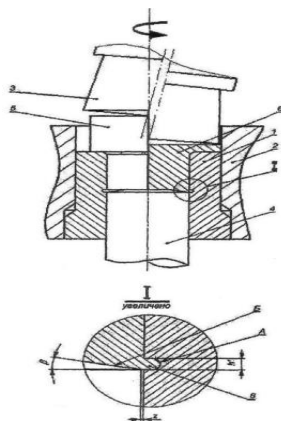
Пристрій для ШО і виштовхування заготовок з тонким фланцем:
